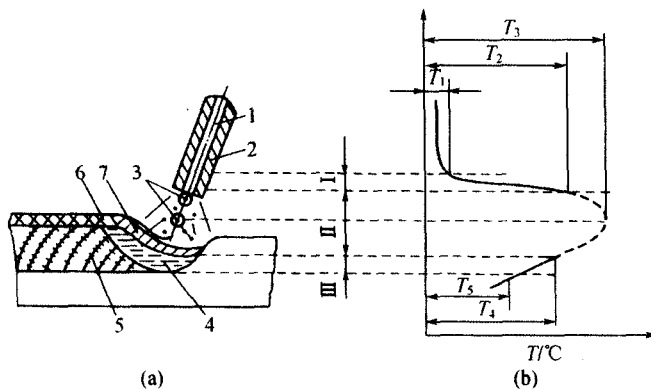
焊接冶金反应区(以药皮焊条为例)
